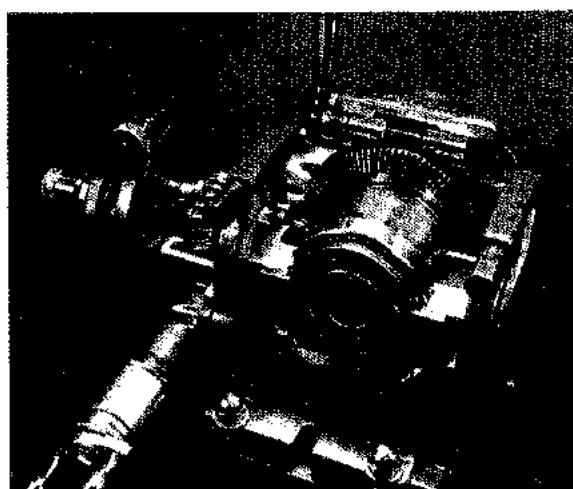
Cabezal divisor universal provisto de rueda en espiral, con relación 5:1 entre el husillo y la manivela de división (Kearney & Trecker Corp.)
